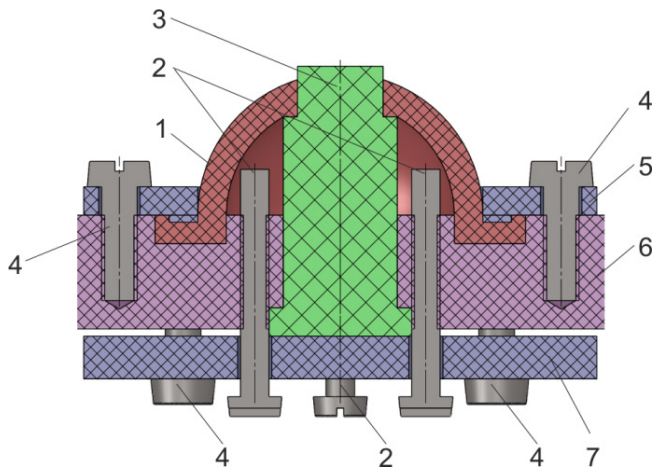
Funktionsmuster: 1 Tastkörper; 2 Elektroden=Schrauben; 3 Verformungskörper; 4 Befestigungsschrauben; 5 oberer Befestigungsring; 6 Kunststoffplatte; 7 unterer Befestigungsring
